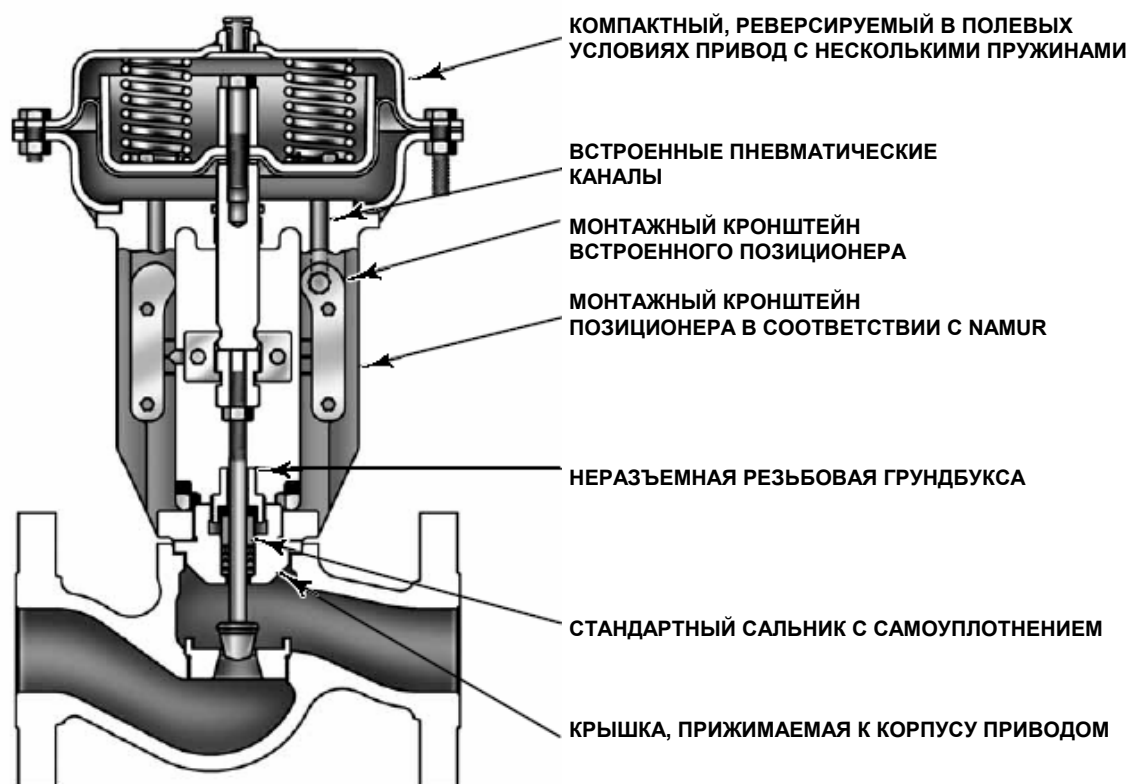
клапан конструкции GX с направляющей штока и профилированным плунжером (размер DN25 / 1 дюйм).
